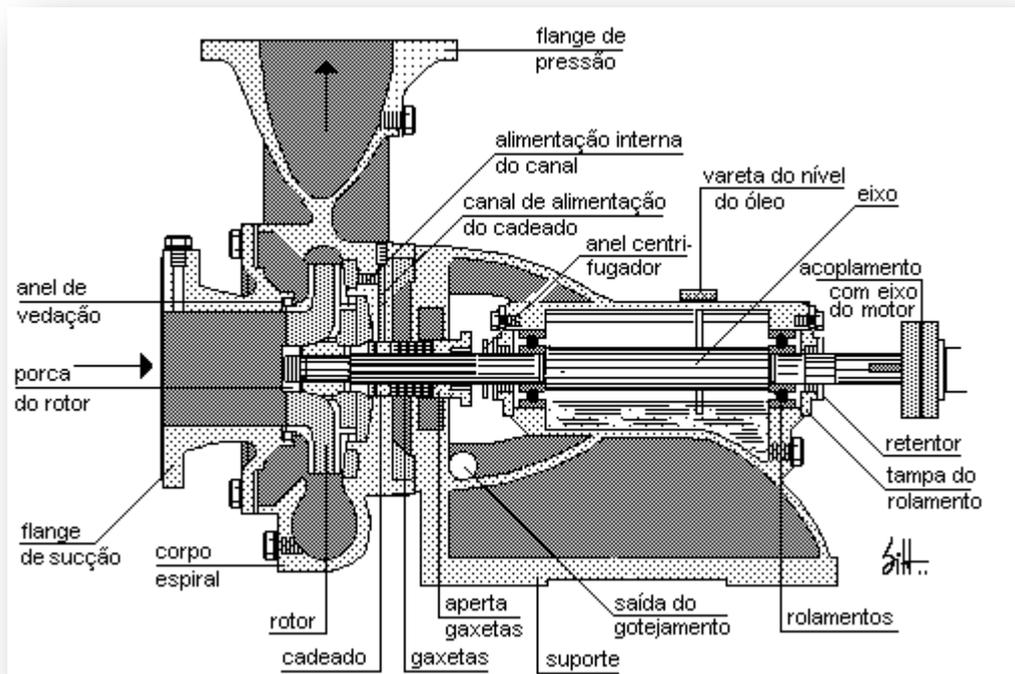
Corte esquemático de uma bomba centrífuga típica
